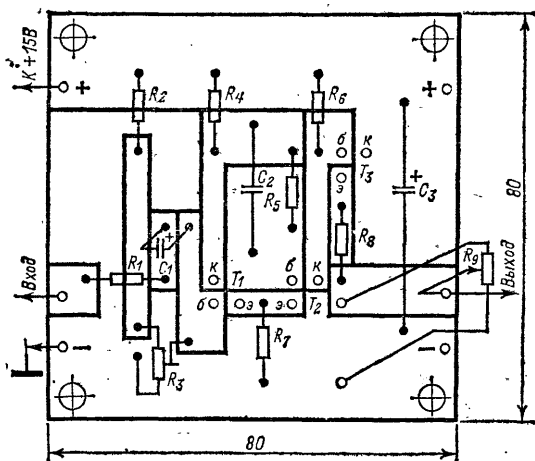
Чертеж печатной платы формирователя прямоугольного напряжения.
